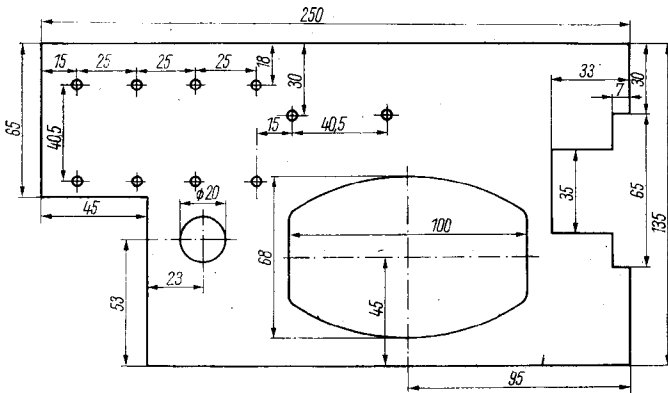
Maßskizze des Chassisbleches bei Verwendung des Lautsprechers L 2160 PO. Befestigungsbohrungen und Durchbrüche für die Filter (Bild 11) der Übersichtlichkeit wegen weggelassen
